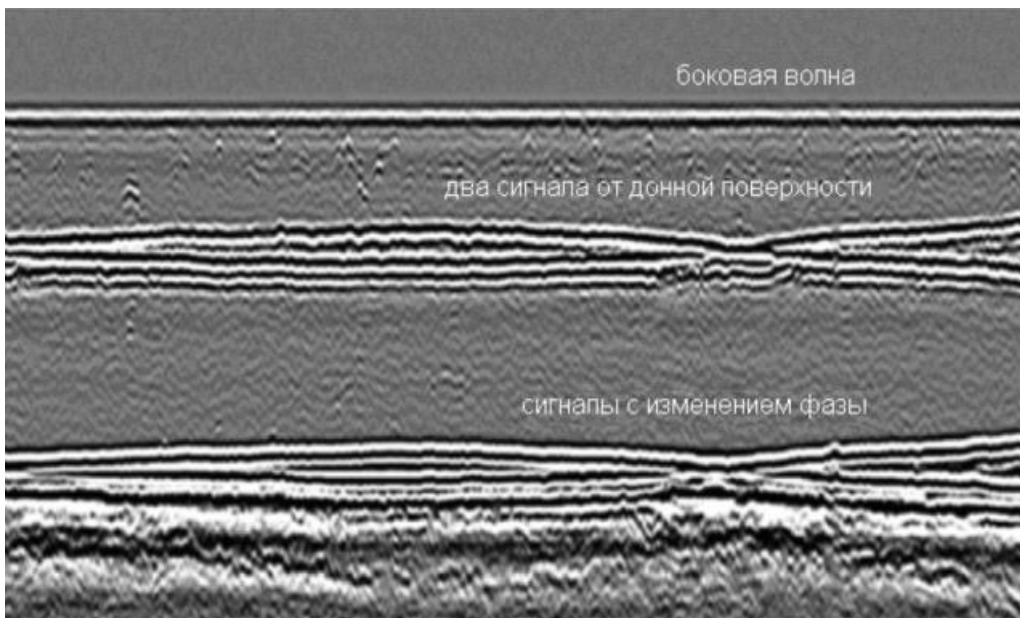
Изображение смещения труб с кольцевыми сварными швами
